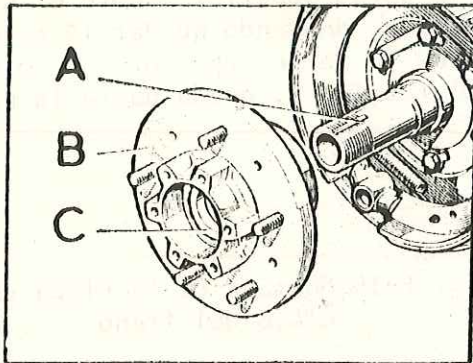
Desmontaje del conjunto del buje delantero y cojinete
